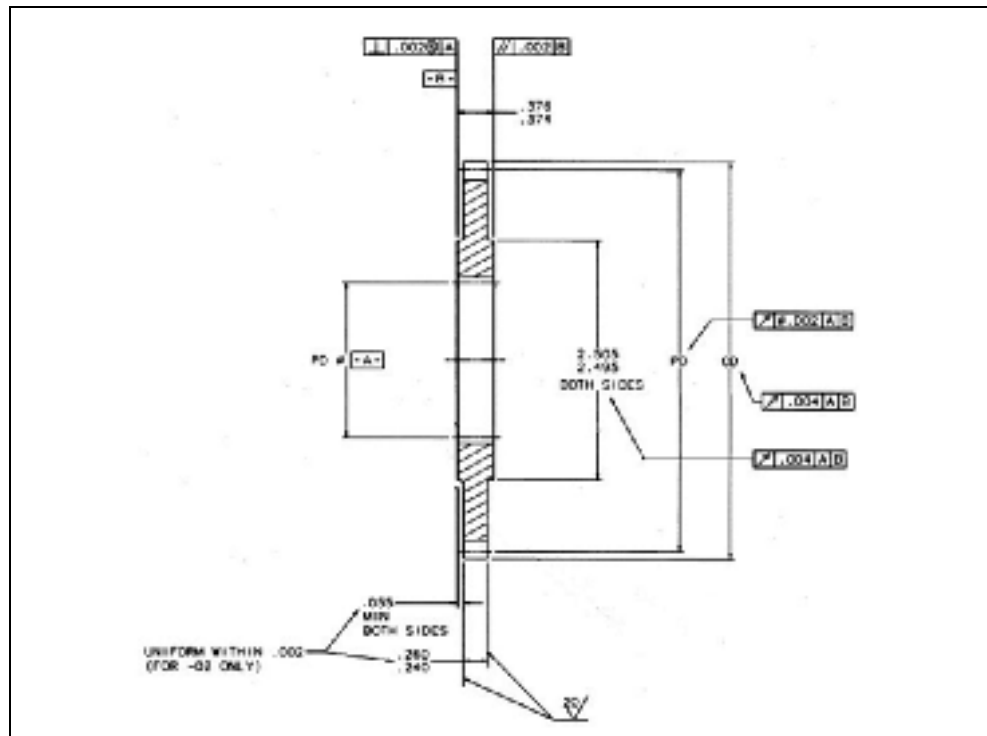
Extrait dessin de définition « 1280 » - tolérances des plans et du diamètre extérieur (dimensions en pouces)
